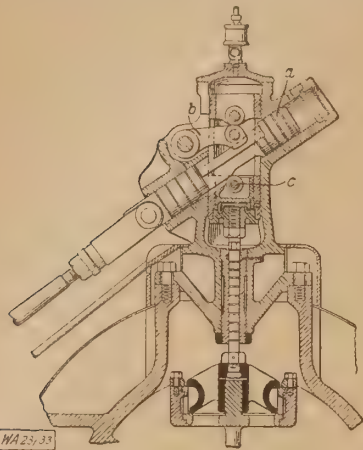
Ventilsteuerung für Gleichstrom-Dampfmaschinen.
